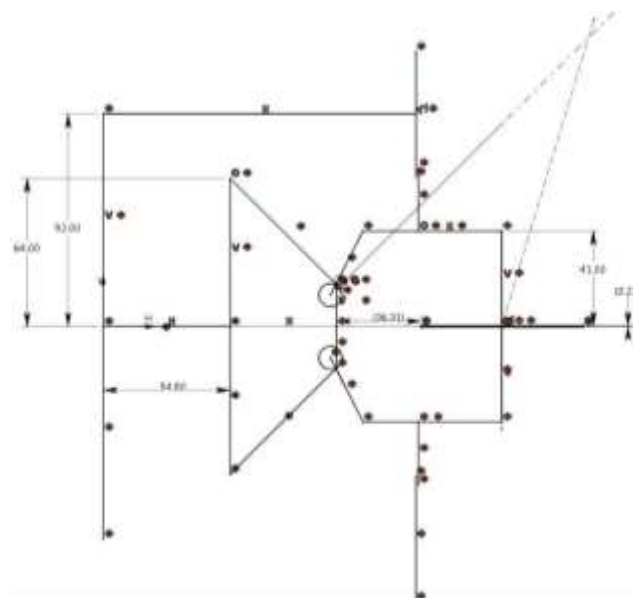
Esquema pilotante 1, posición cerrada, Fuente: propia
